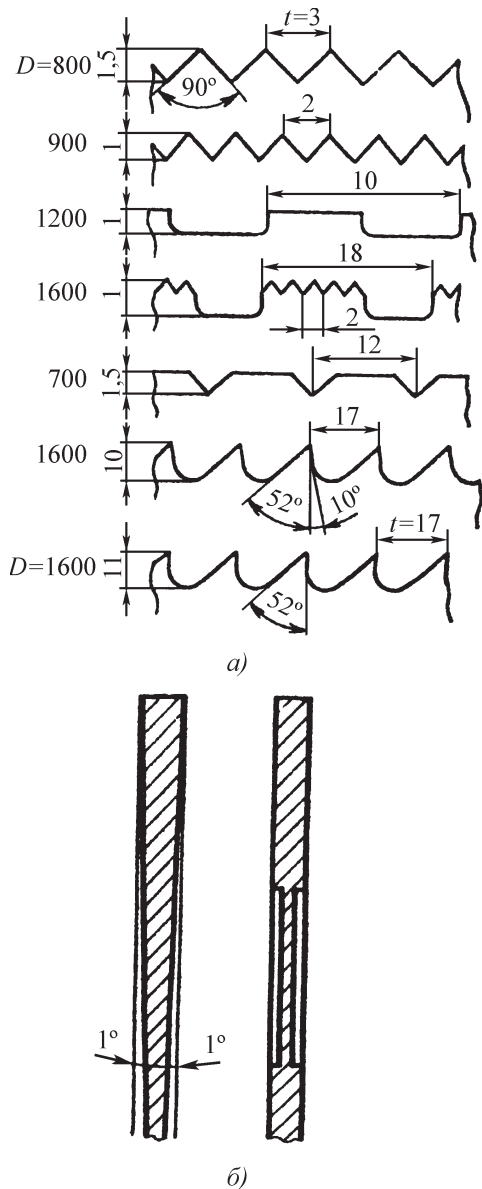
Форма зубьев режущей кромки дисков (а), виды поднутрения (б)
